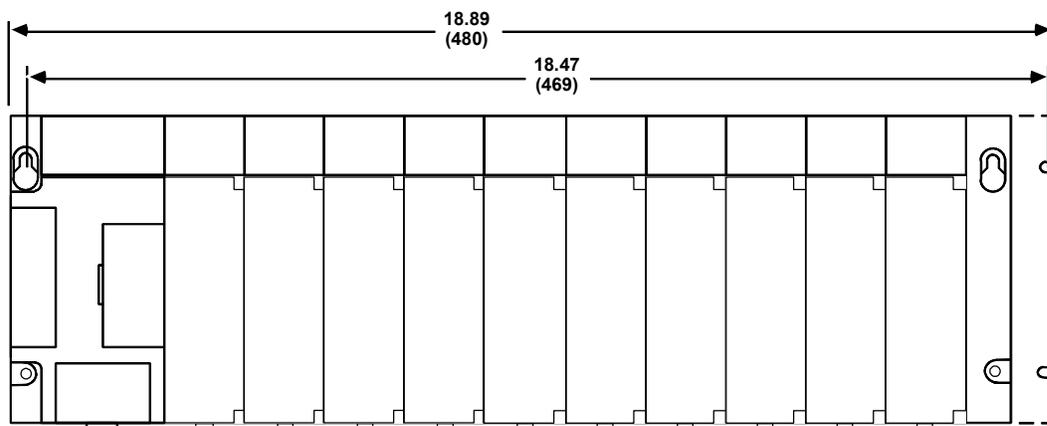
Dimensiones para el montaje en un rack de 19" utilizando un soporte adaptador IC693ACC308
